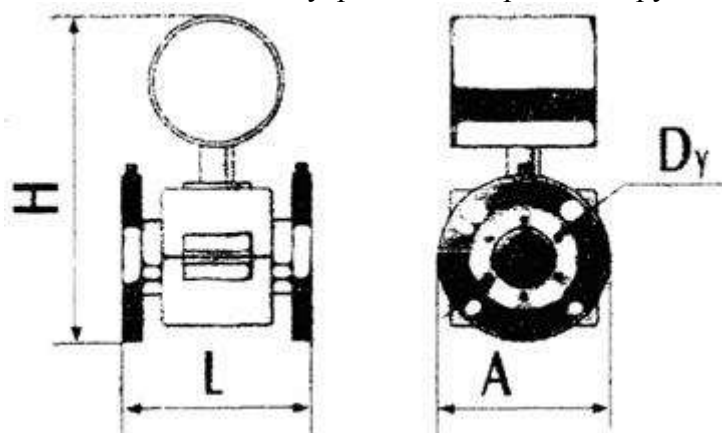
Конструкция счетчика электромагнитного типа: H, L, A, Dy - присоединительные и габаритные размеры.
